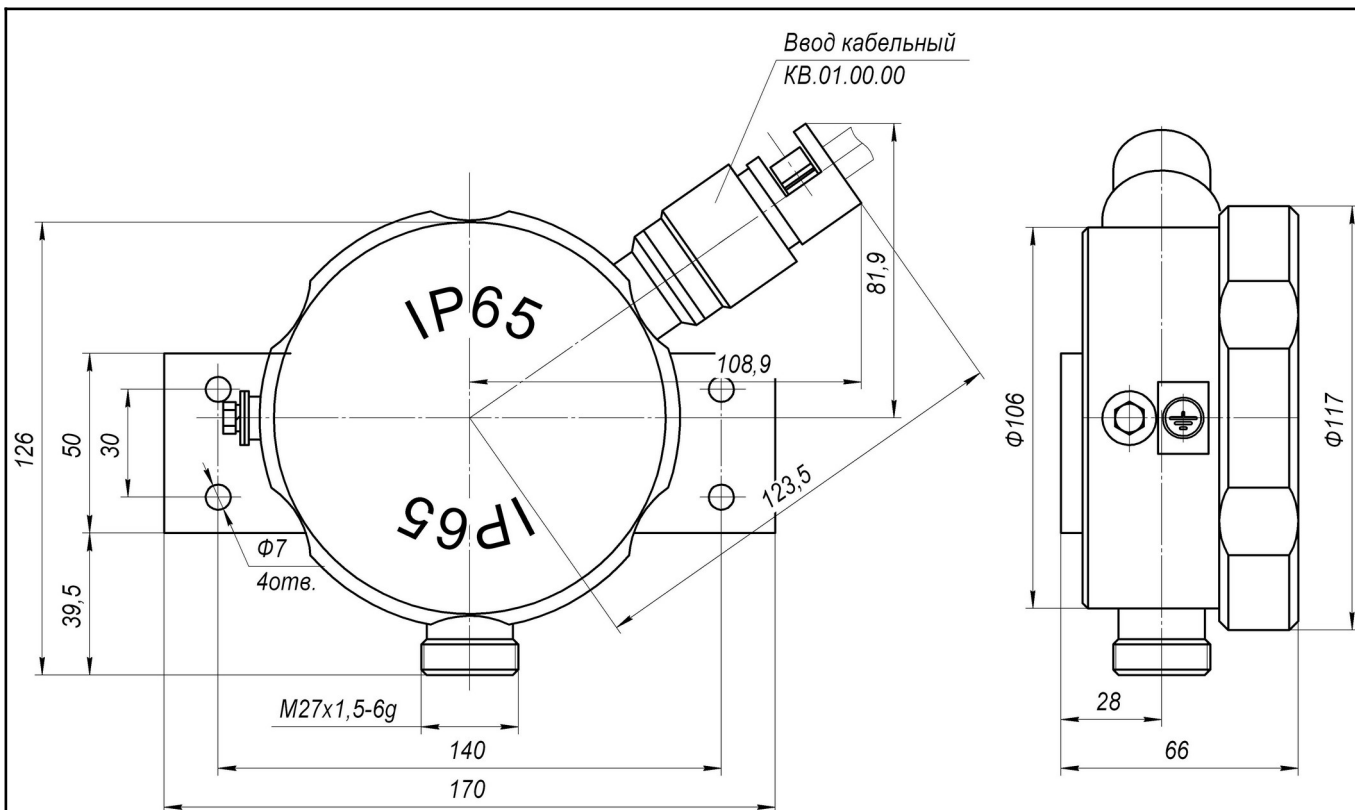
Корпус «Н» ЭБ ПП из стали 12Х18Н10Т
